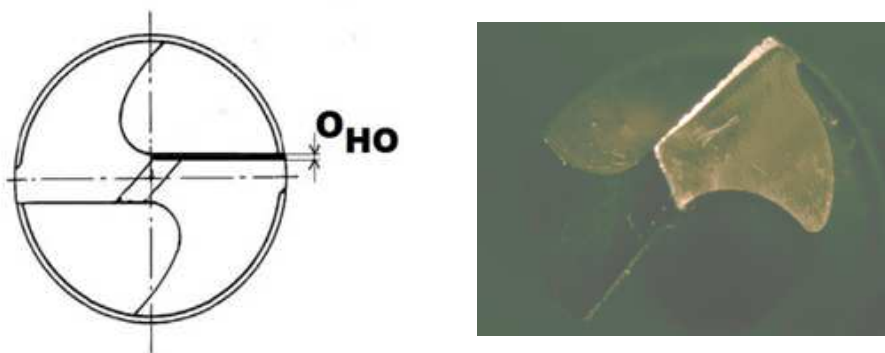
Frézování - opotřebení na hlavním hřbetu
